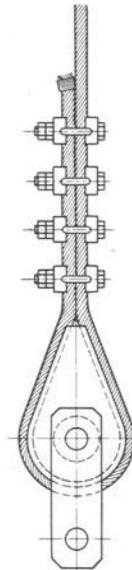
Seileinband mit Kausche und Klemmbügeln.
